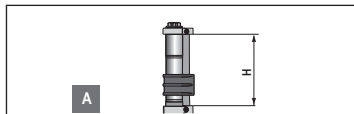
Installazione sul telaio di forcelle a doppia piastra: (2A) Lunghezza canotto di sterzo tra le piastre
